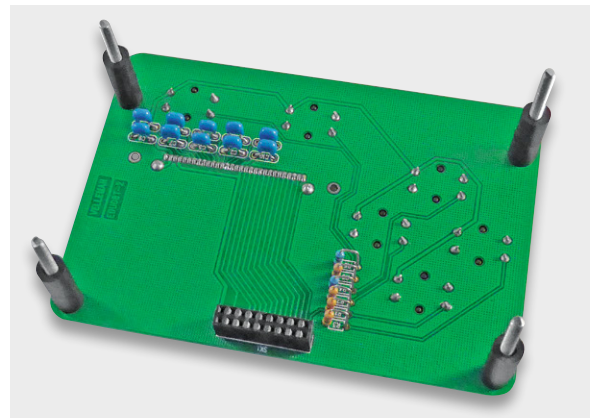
So sind Befestigungsschrauben und Distanzhülsen einzusetzen.
